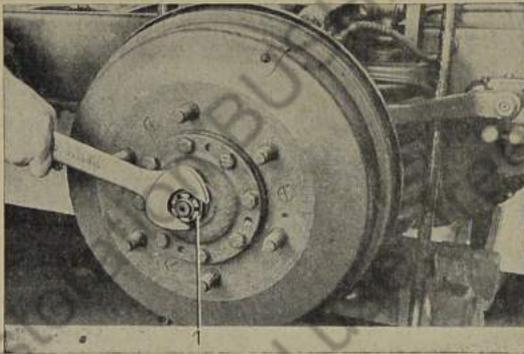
Kronenmutter von Quergelenkwelle abschrauben
